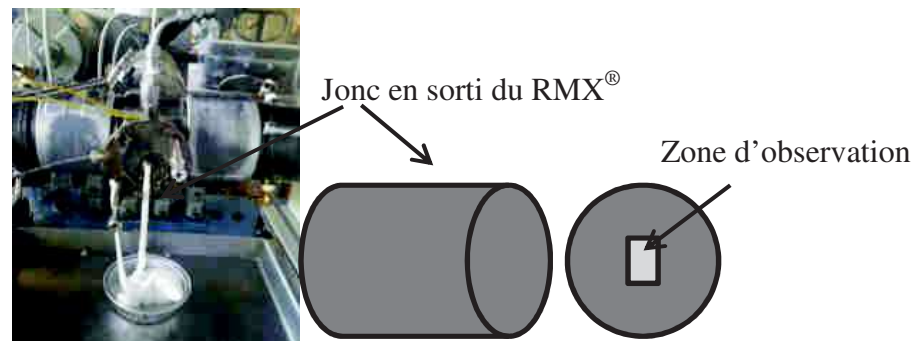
Zone d'observation sur le jonc sorti du RMX® (échelle 2:1)
